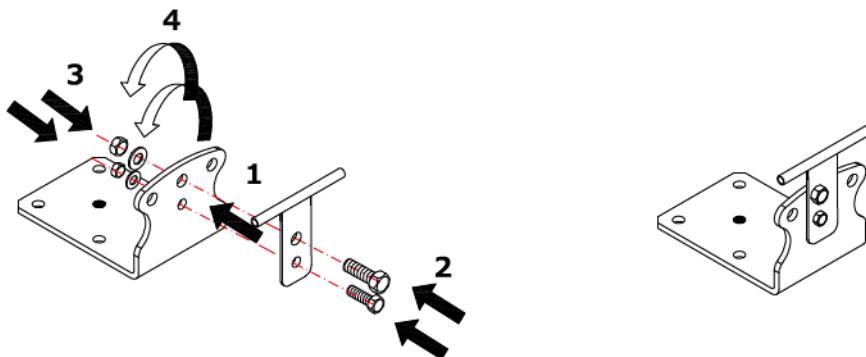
Assemblaggio del dispositivo LVB/LVBD con passacavo dritto fisso per navetta (Cod. 001346)
